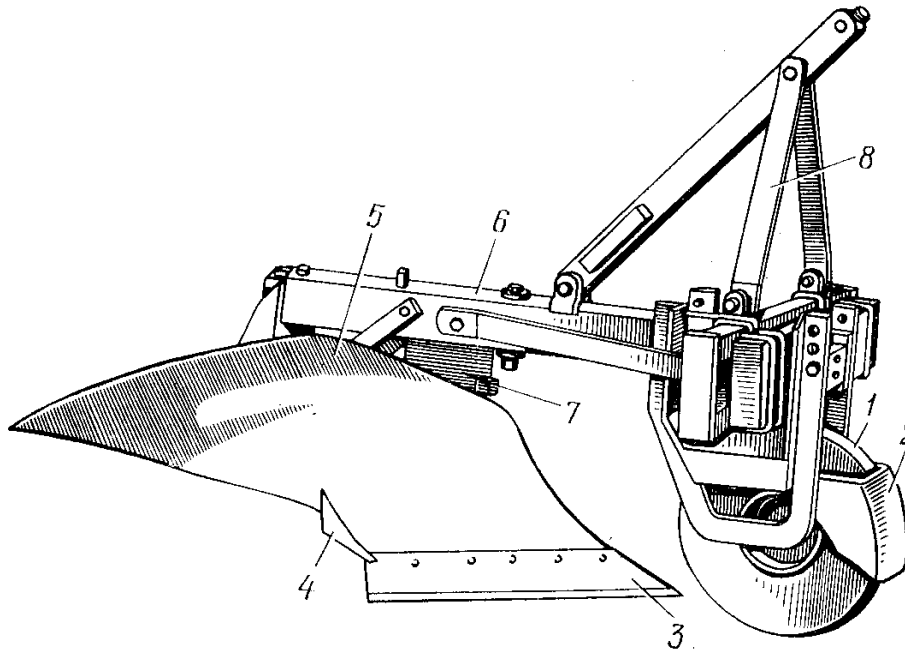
Плуг ПКЛ-70 (с одноотвальным корпусом): 1 — дисковый нож; 2 — защитный лобовик; 3 — лемех; 4 — боковой подрезной нож 5 — отвал; 6 — рама; 7 — стойка; 8 — устройство для навески
